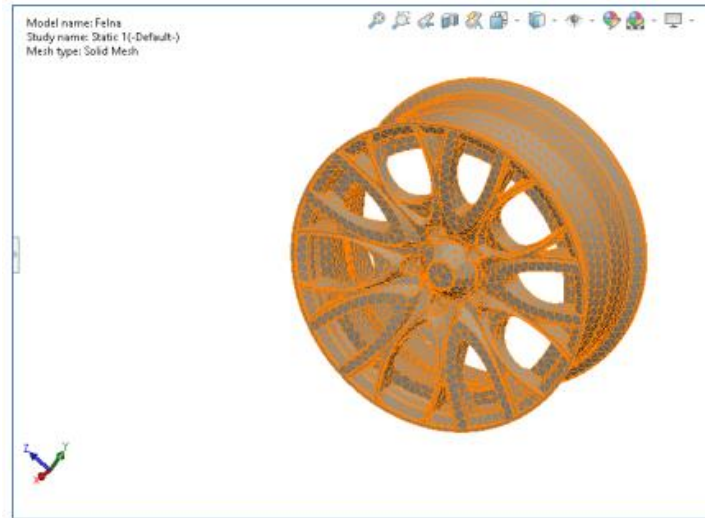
Виготовлення сітки конструкції краю колеса авто.
